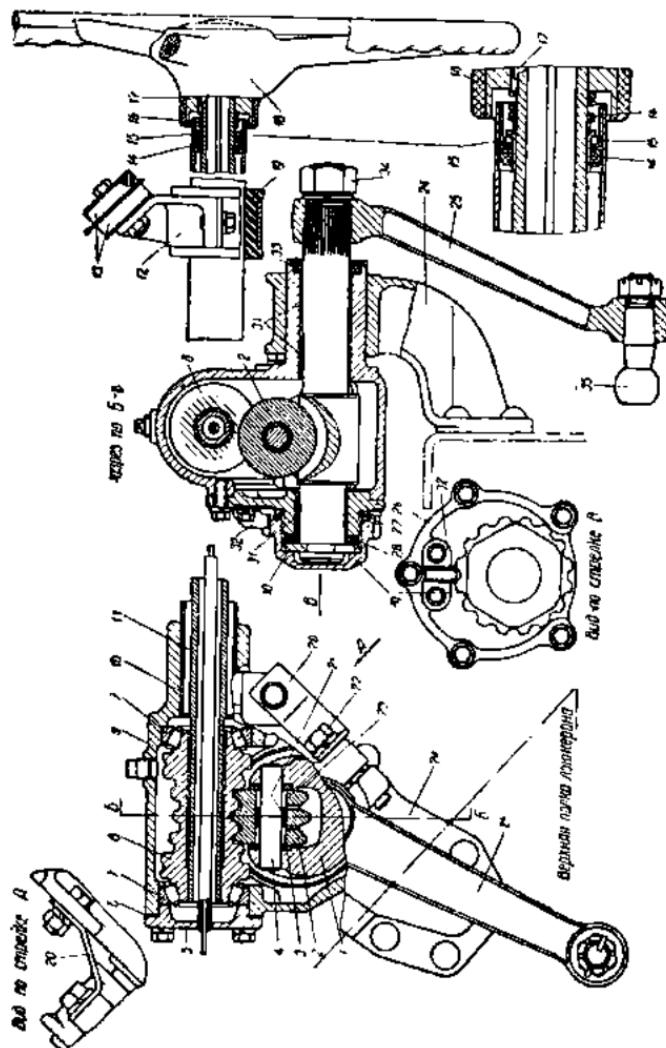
Рулевой механизм. {1 — вал рулевой сошки; 2 — ролик; 4 — ось ролика; 6 — подшипники червяка; 7 — червяк; 10 — труба рулевой колонки; 11 — рулевой вал; 12, 13 и 19 — детали крепления рулевой колонки к щитку; 15 — верхняя опора рулевого вала; 25 — рулевая сошка; 27, 28, 29, 30 и 32 — детали регулировочного устройства в зацеплении червяка и ролика).
